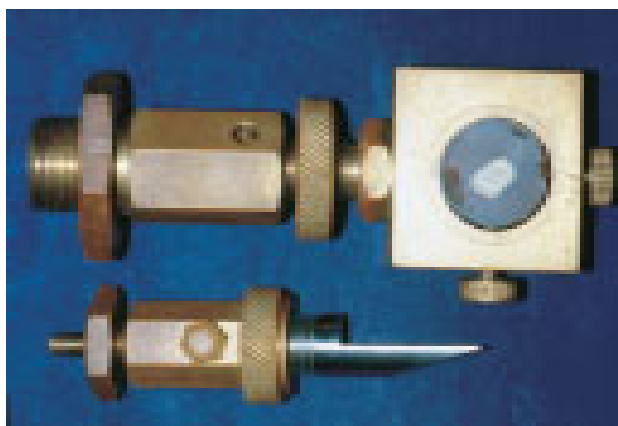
Garra posicionadora do corpo-de-prova na máquina EMIC
